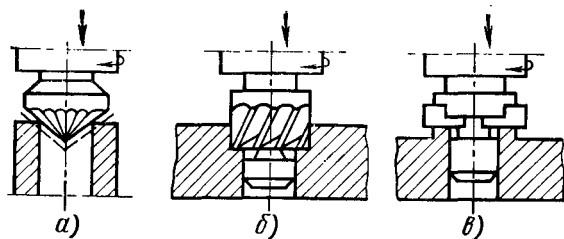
Зенкерование торцевых поверхностей: а — зенковка; б — цековка с несколькими зубьями и направляющей цапфой; в — цековка со вставными зубьями и направляющей цапфой
